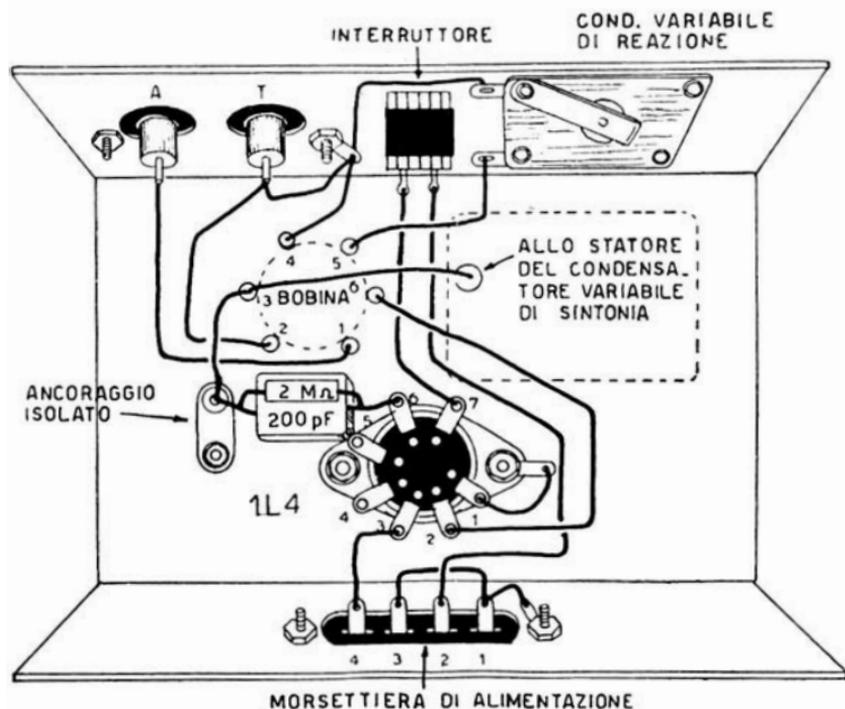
Cablaggio sotto il telaio del ricevitore di fig. 14.1.
